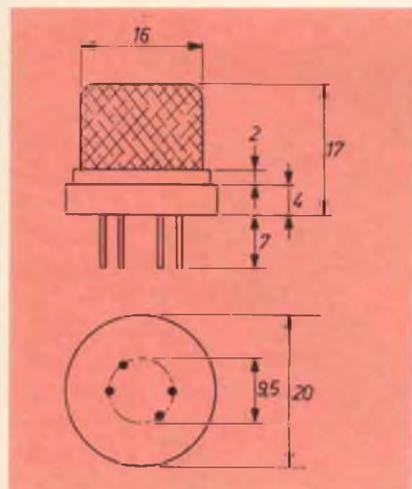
Dimensioni del semiconduttore sensibile al gas mod. CL-10.
